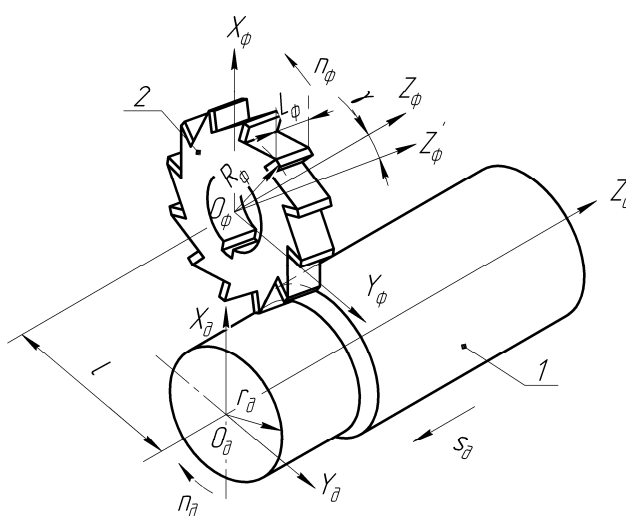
Схема фрезерування циліндричного вала зі схрещеними осями інструмента та деталі
